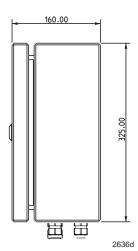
Grupo de alimentación Control Power Box: vista posterior y lateral
